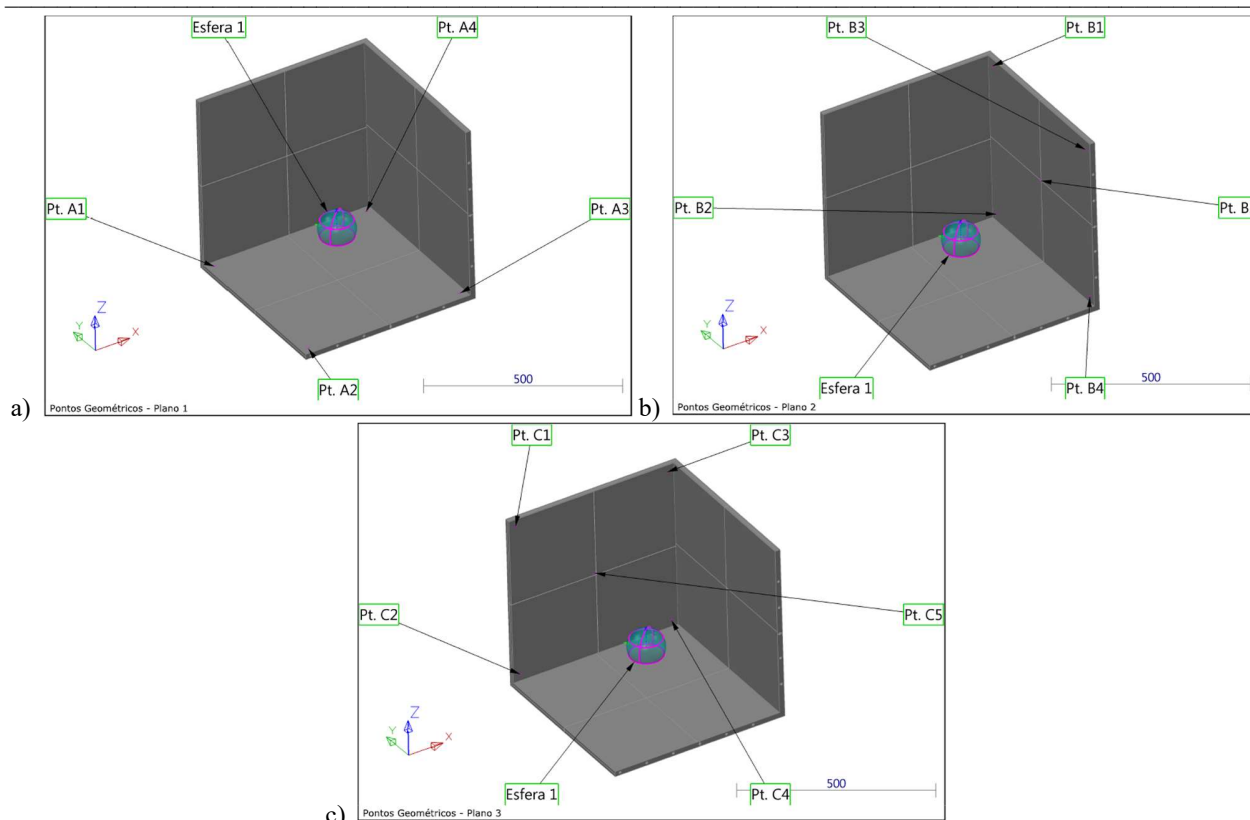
a) Pontos medidos A1 a A4 sobre o Plano 1; b) Pontos medidos B1 a B5 sobre o Plano 2 e c) Pontos medidos C1 a C5 sobre o Plano 3.
